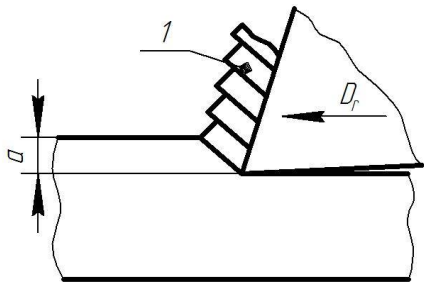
Схема стружкоутворення: *a* – шар, що зрізається; 1 – стружка
